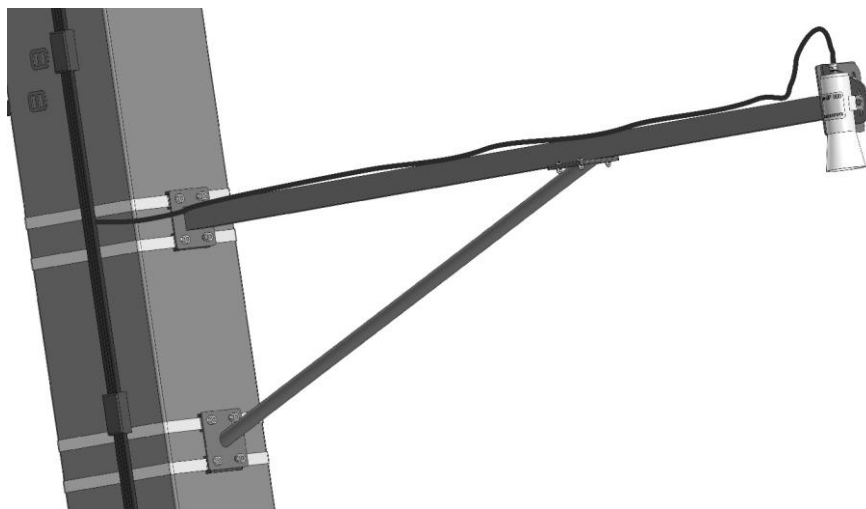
Внешний вид установленного Сокол-ДР 800.
